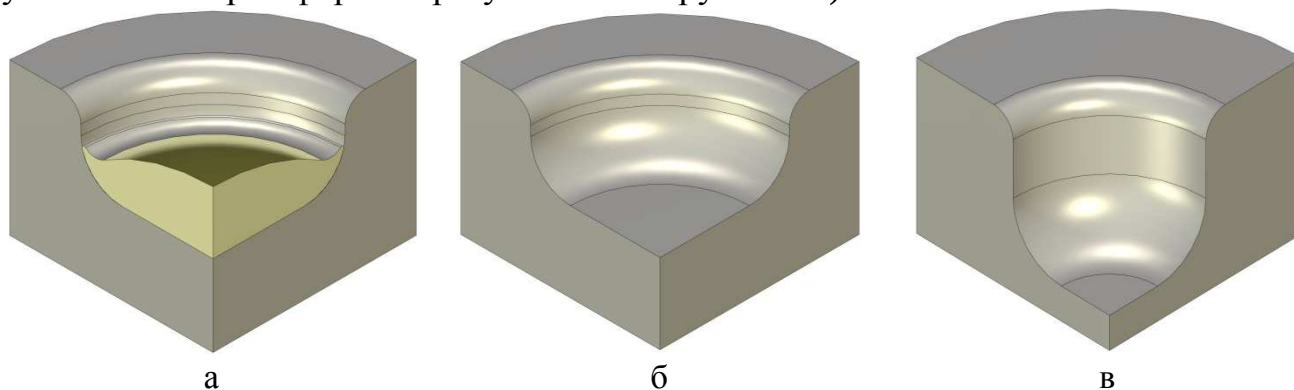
Модели технологической оснастки: промежуточная матрица и реверсивный вкладыш (а), промежуточная матрица (б), матрица конечного формоизменения заготовки (в)
